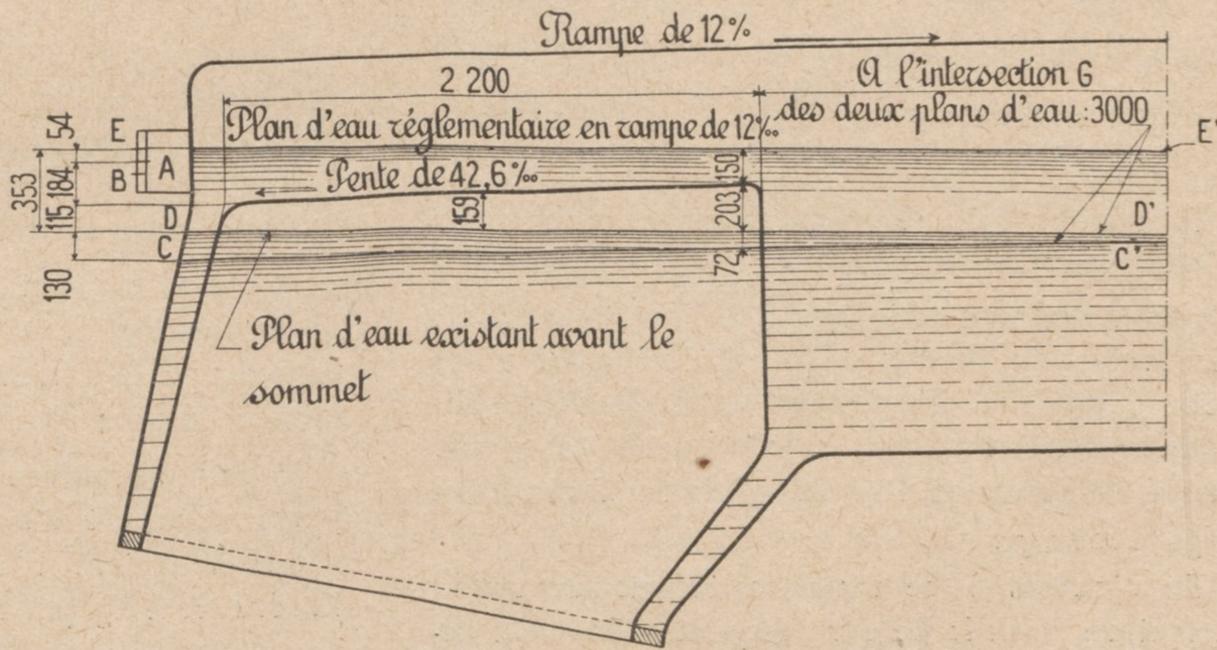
Position présumée du plan d'eau DD' avant le sommet de la rampe la machine étant en rampe de 12 %
